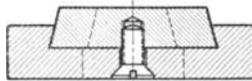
Befestigung der Schnittplatte durch Schwalbenschwanz und Zugschraube.
